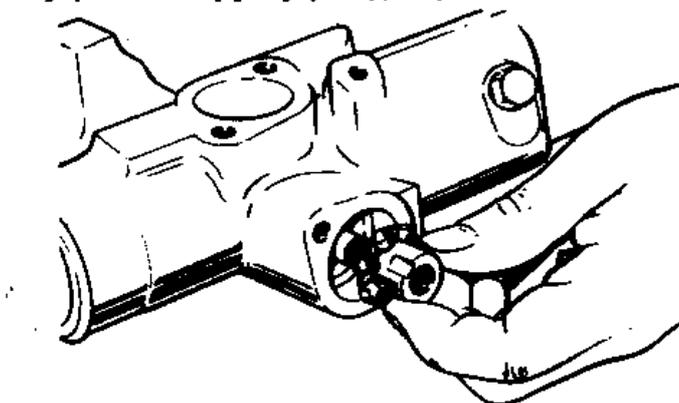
Нижний подшипник навинчивается на шестерню (Разд.35)
